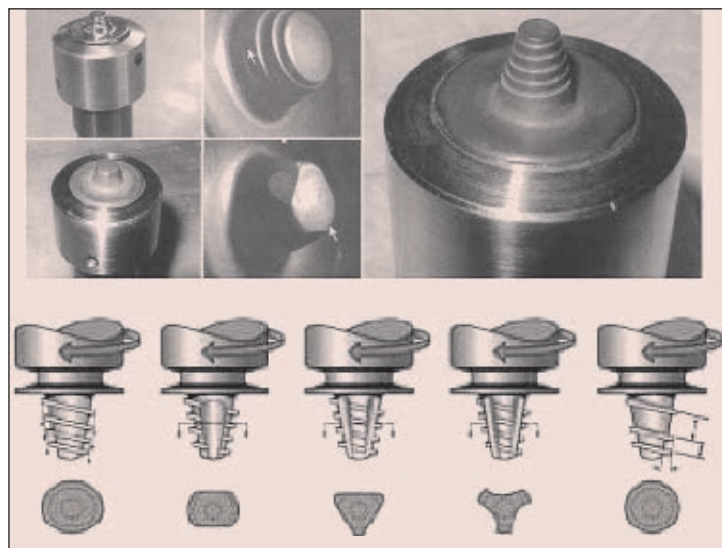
Некоторые варианты конструкций рабочего инструмента для сварки трением с перемешиванием различных типов соединений
